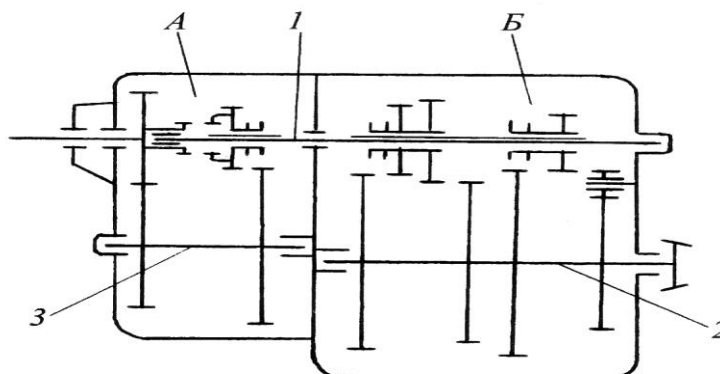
Составная коробка передач: А – редуктор; Б – основная коробка передач; 1 – вторичный вал редуктора; 2 – вторичный вал коробки; 3 – промежуточный вал редуктора
